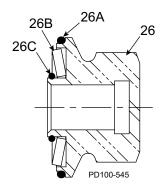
Vue en coupe de l'assemblage de l'écrou du rotor, tel qu'il est assemblé
